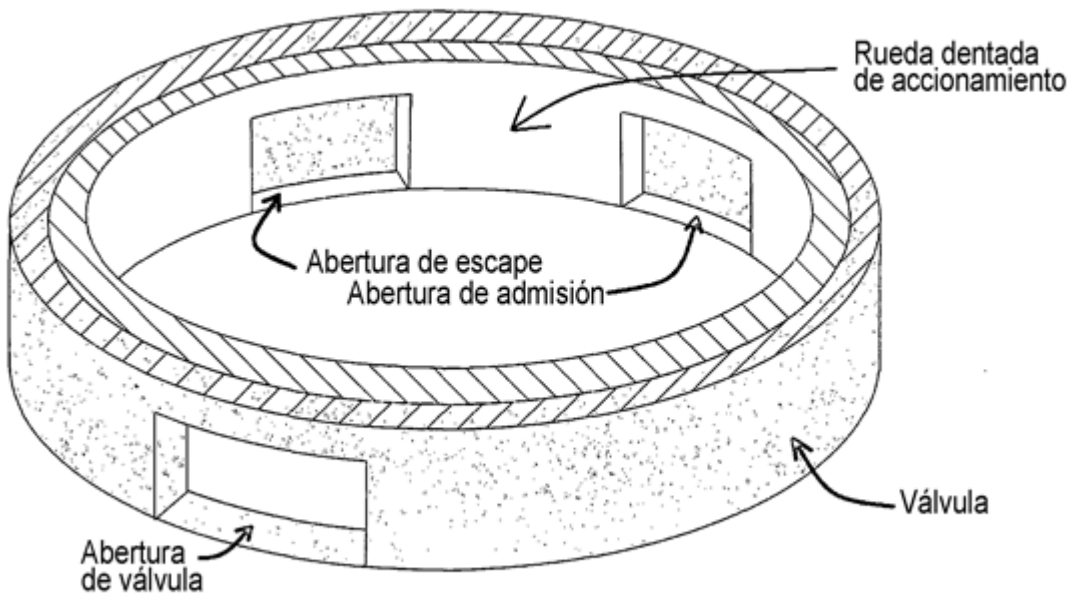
Sección transversal de una válvula y una pared de cilindro en el estado cerrado
